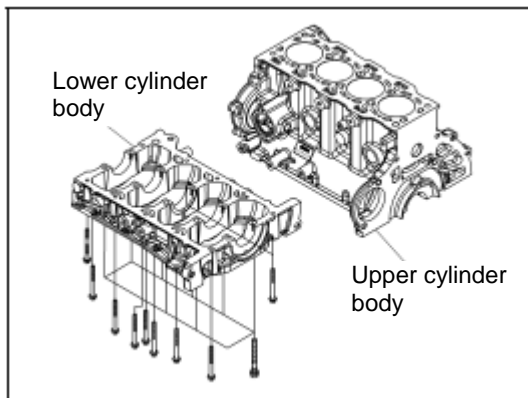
裝配上缸體 Fig. 5-20-18
